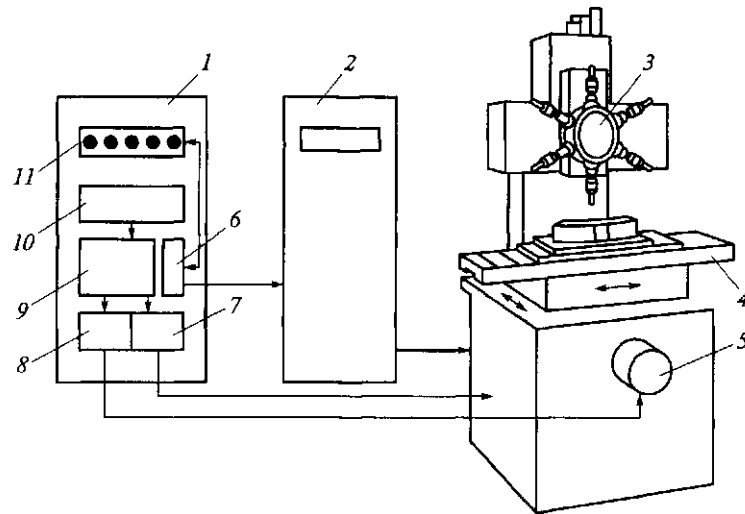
Вертикально-сверлильный станок с ЧПУ:
